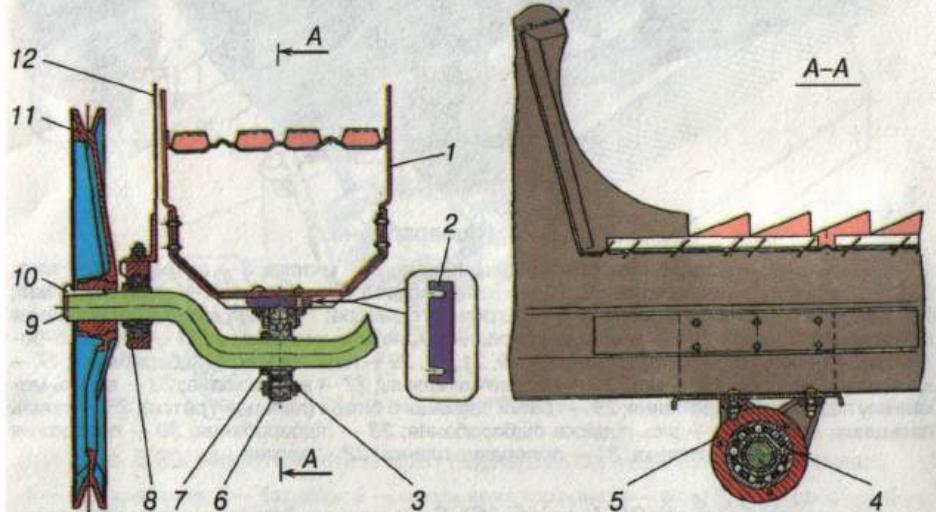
Вал колінчастий ведучий соломотряса:
